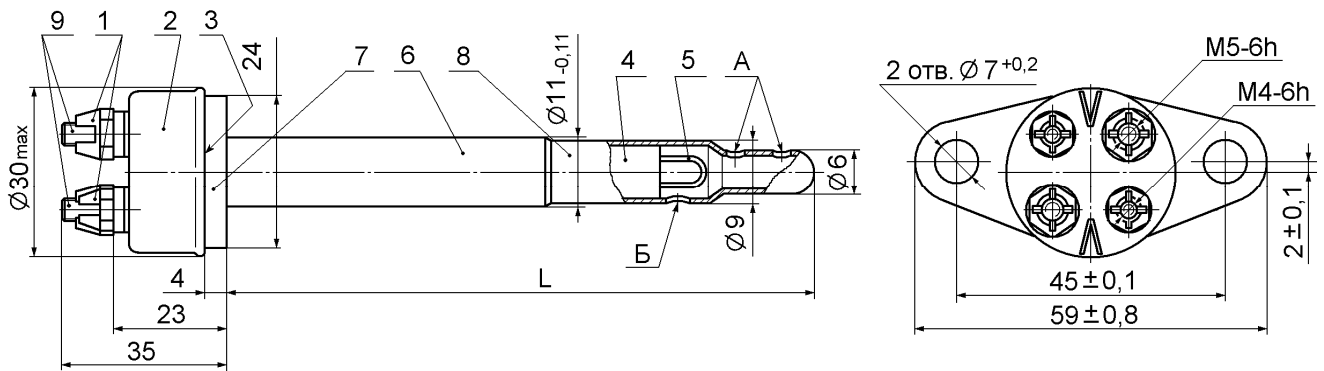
Габаритный чертеж термопреобразователей ТХА-75, ТХА-100
